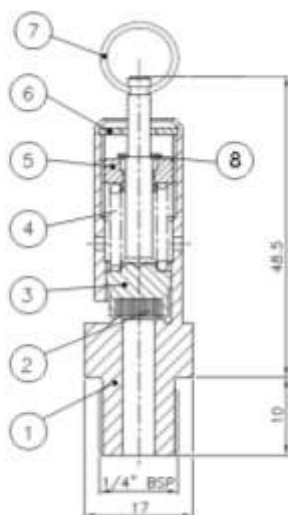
Клапан предохранительный: 1 – корпус; 2 – уплотнение; 3 – шток; 4 – пружина; 5 - регулятор; 6 - проволока и пломба; 7 – подъемное устройство; 8 - кольцо стопорное; 9 – выход организованного дренажа.
